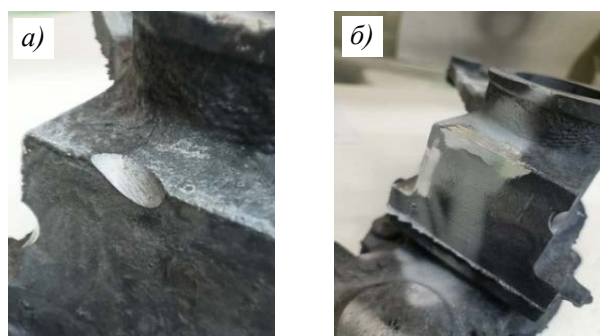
Отливка «Корпус» до (а) и после напыления (б)
